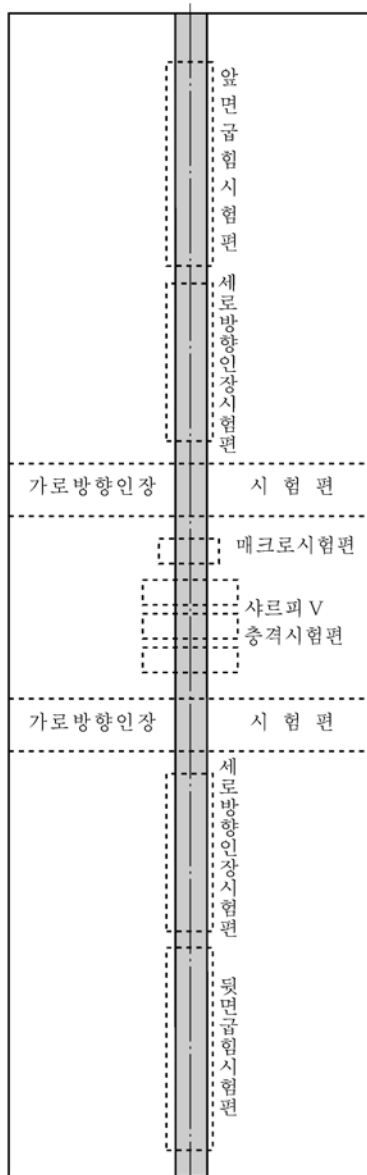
용접절차 인정시험의 시험재의 모양 및 치수 (단위 : mm) (계속)
